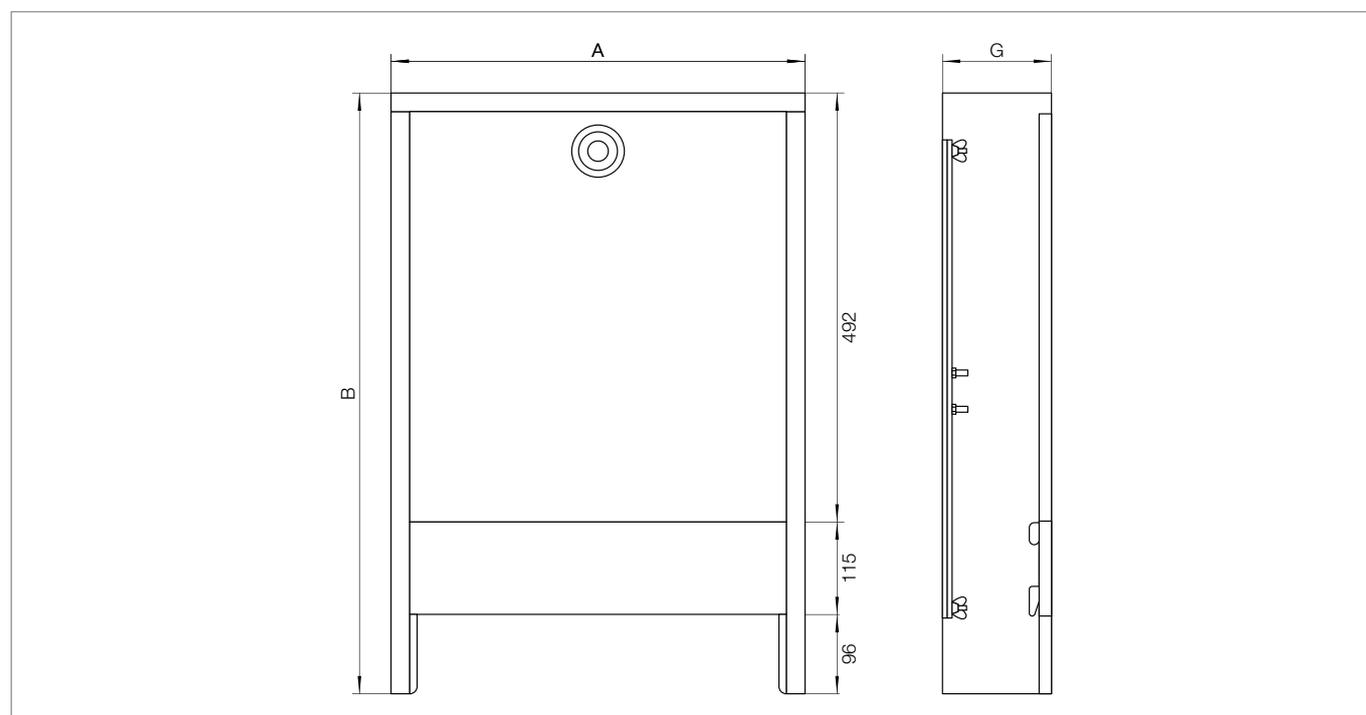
Dimensions coffret pour collecteur AP 130
